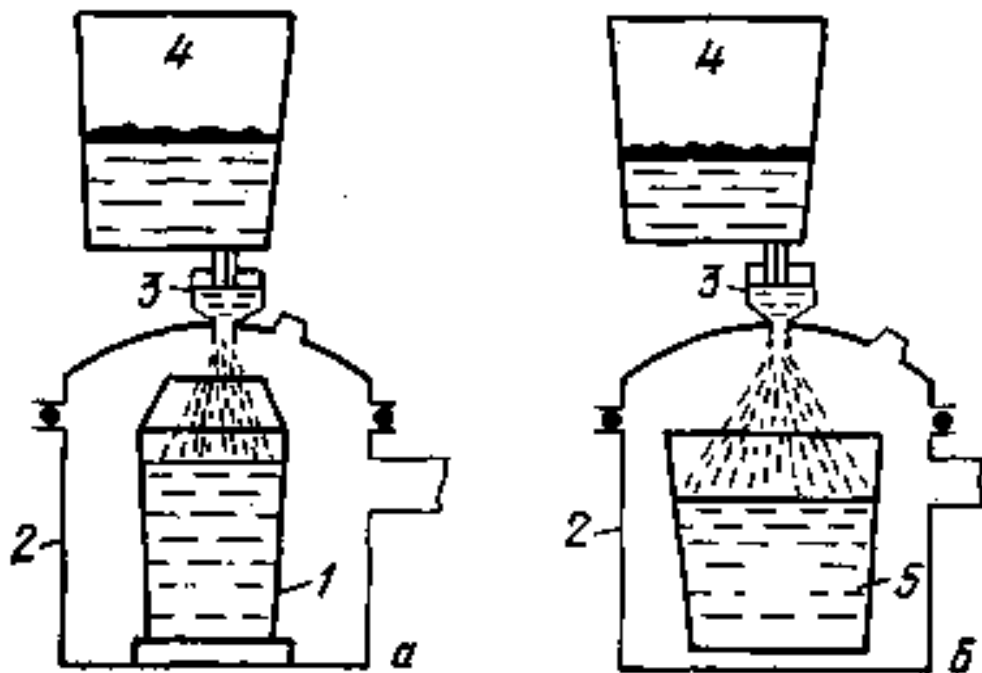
Установки вакуумування в струмені: а - при відливанні зливку; б - при переливі з ковша в ківш; 1 - виливниця; 2 - вакуумна камера; 3 - проміжна ємкість; 4 - ківш з металом; 5 - сталерозливний ківш
